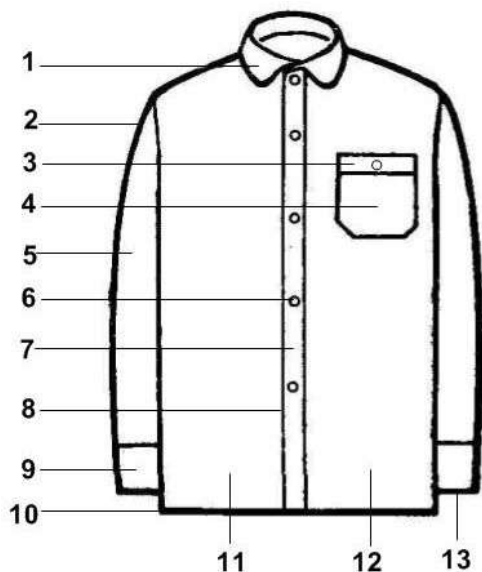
Рубашка: 1) воротник; 2) окат рукава; 3) клапан кармана; 4) карман; 5) рукав; 6) пуговица; 7) планка; 8) срез борта; 9) манжета; 10) низ полочки; 11) правая полочка; 12) левая полочка; 13) низ рукава
